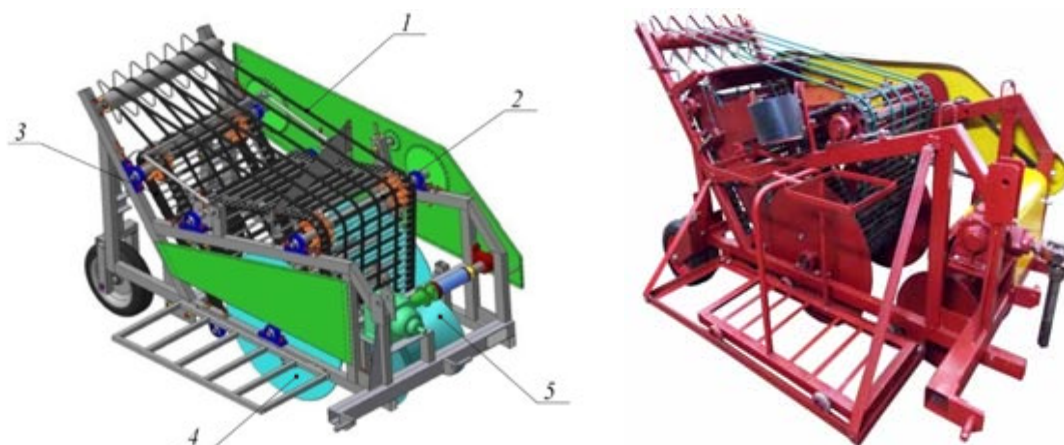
3D модель и опытный образец малогабаритного картофелеуборочного комбайна:
